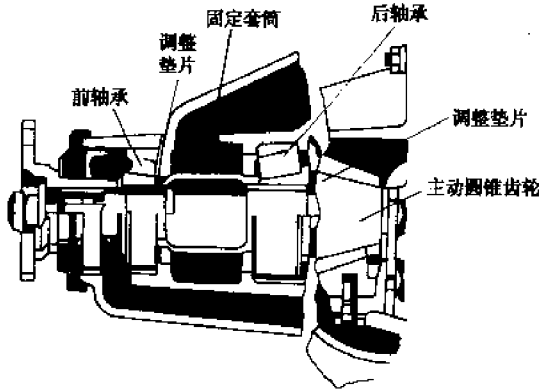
主动圆锥齿轮轴承预紧度的调整方法之一
